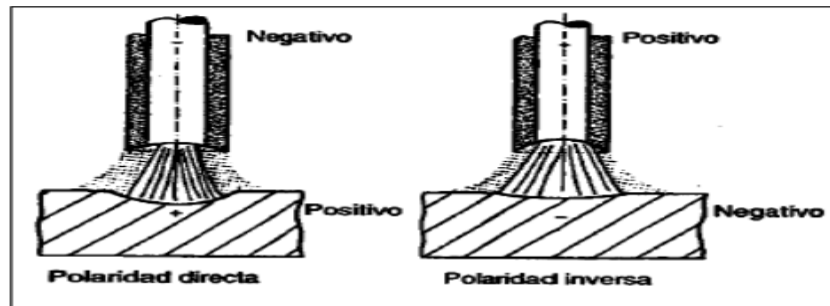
Corriente alterna y continua en la soldadura [43]
